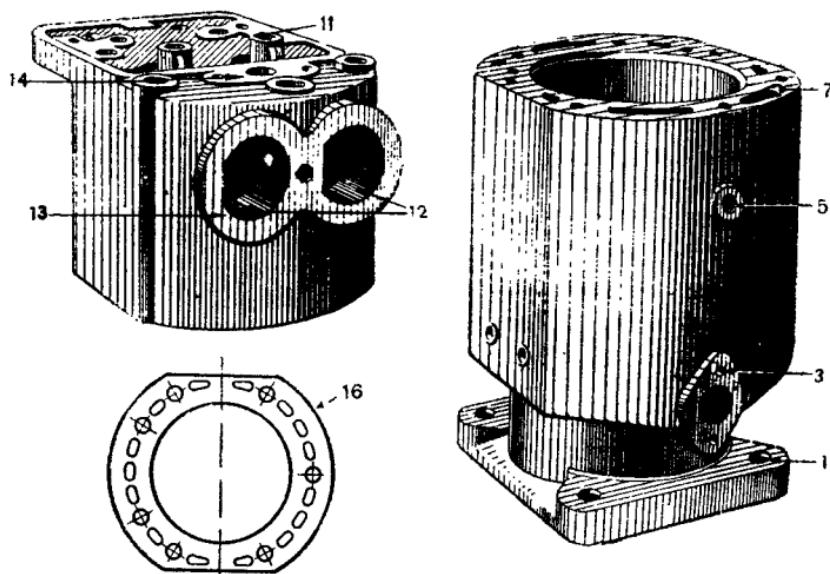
Цилиндр, головка цилиндра и медно-асбестовая прокладка двигателя ЧТЗ.
